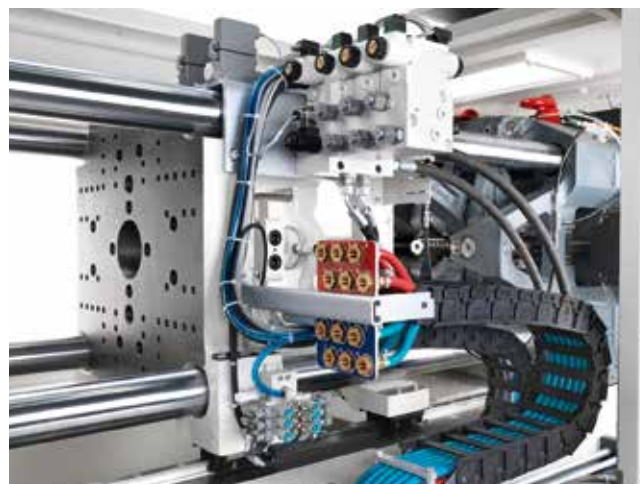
Die PX kann mit werkzeugnahen hydraulischen Kernzugsteuerungen oder Kühlwasserkreisen ausgerüstet und auch nachgerüstet werden (© KraussMaffei)
